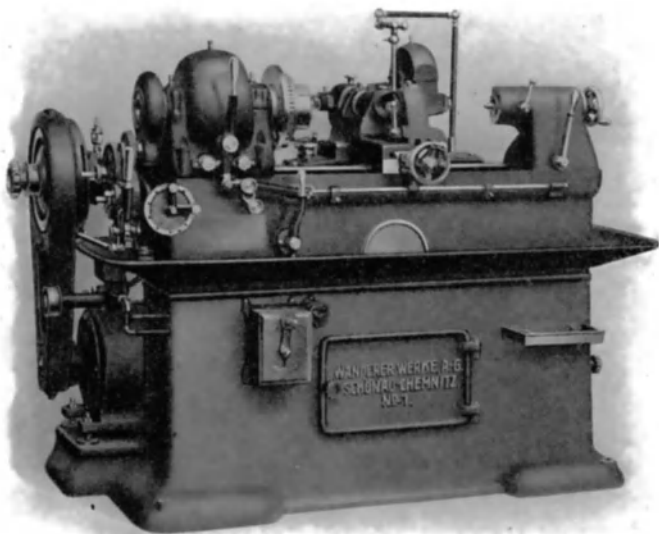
Die Gewindefräsmaschine von Wanderer.
